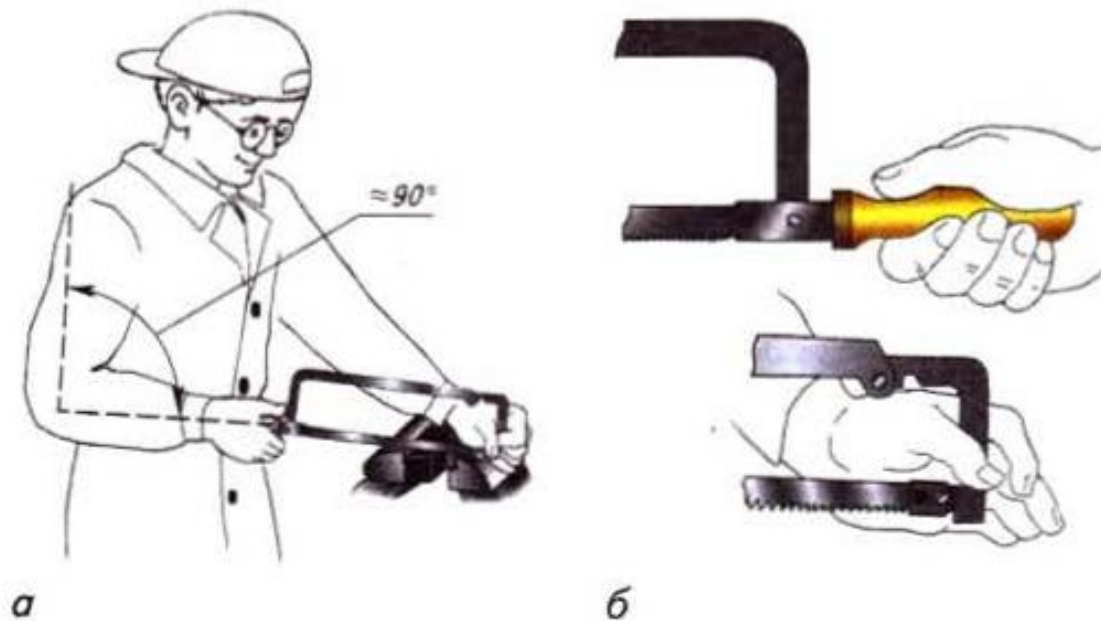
Работа ножовкой: *а* — положение корпуса; *б* — положение рук
